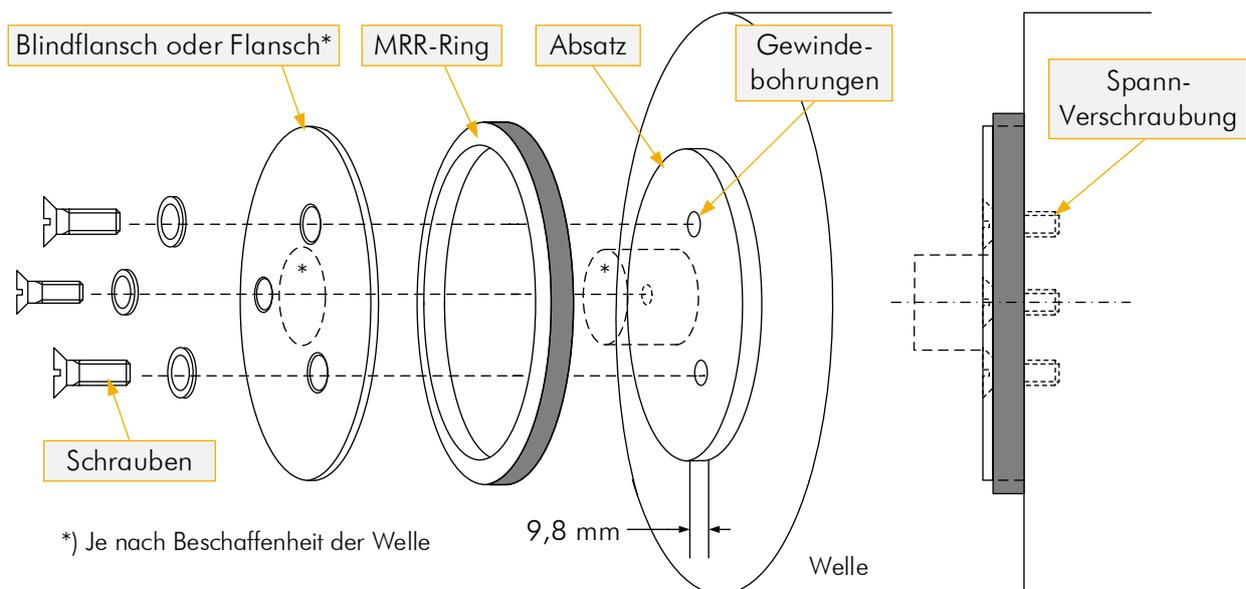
Befestigung mit einem Flansch oder Blindflansch
